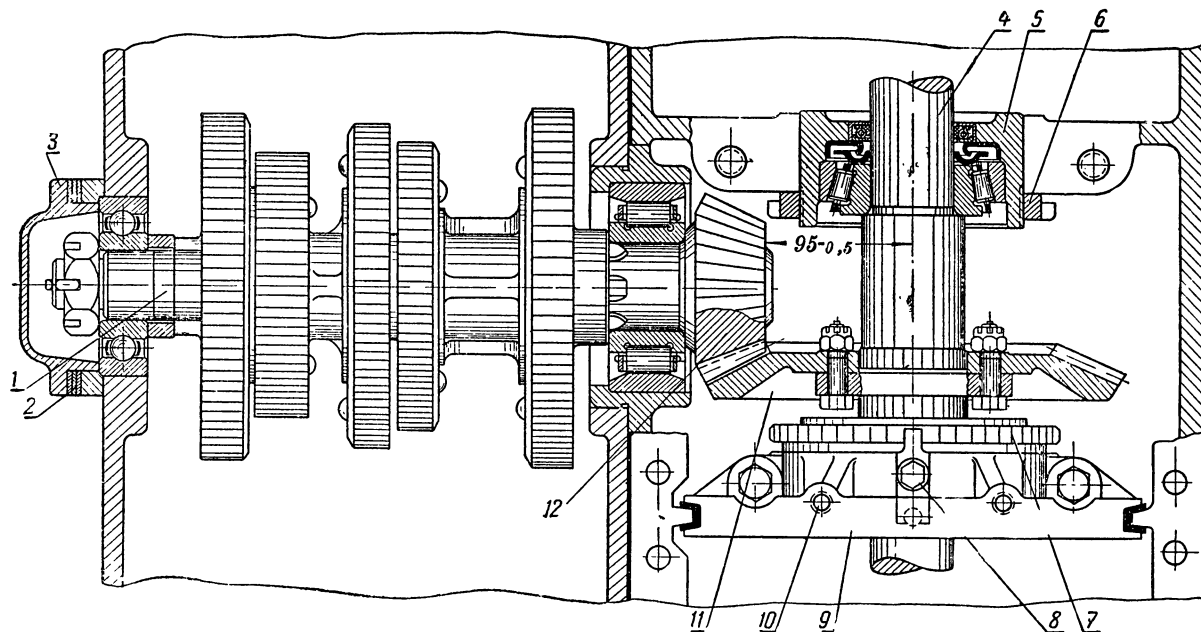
Схема регулировки главной передачи трактора ДТ-54А:
